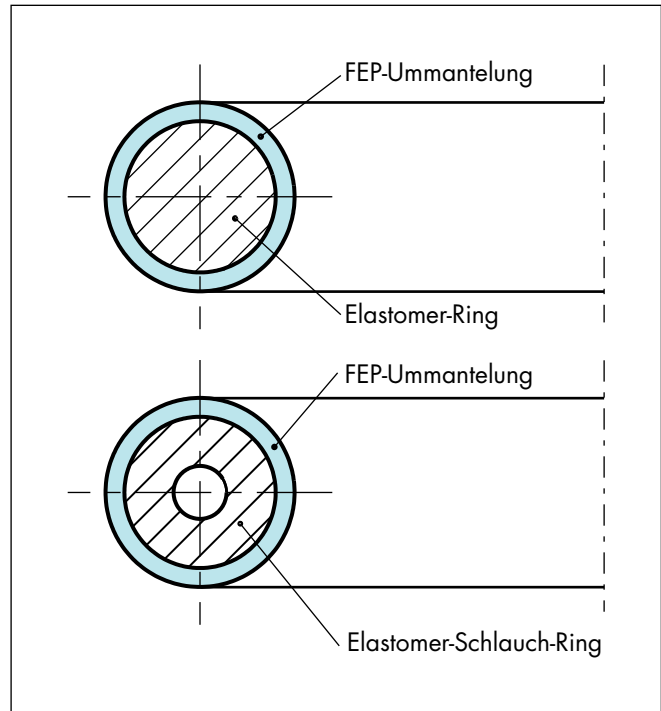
Ausführungen von FEP/PFA-ummantelten O-Ringen
